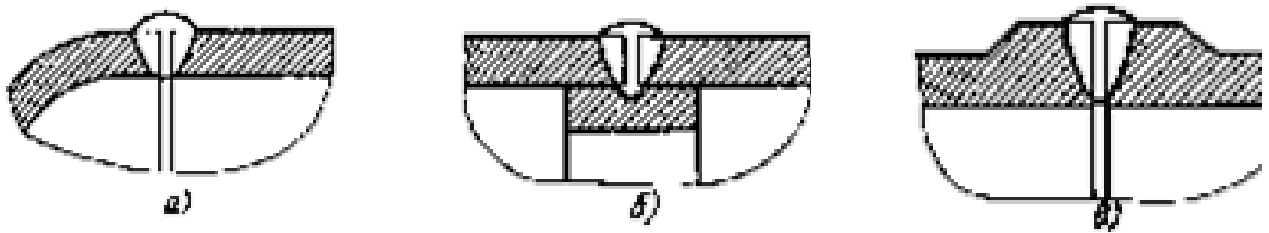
Конструкції кільцевих стикових зварних з'єднань
